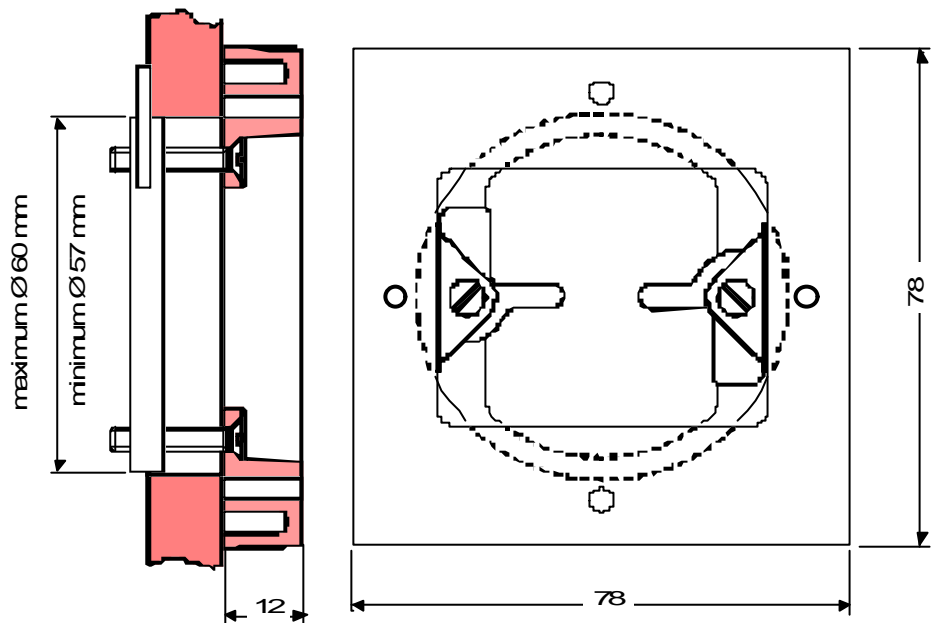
Kit de montage sur panneau (dimensions en mm)
